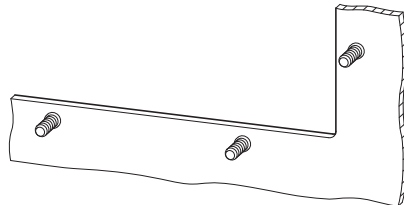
Schweiß-Gewindebolzen M4 x 12 am Blech
